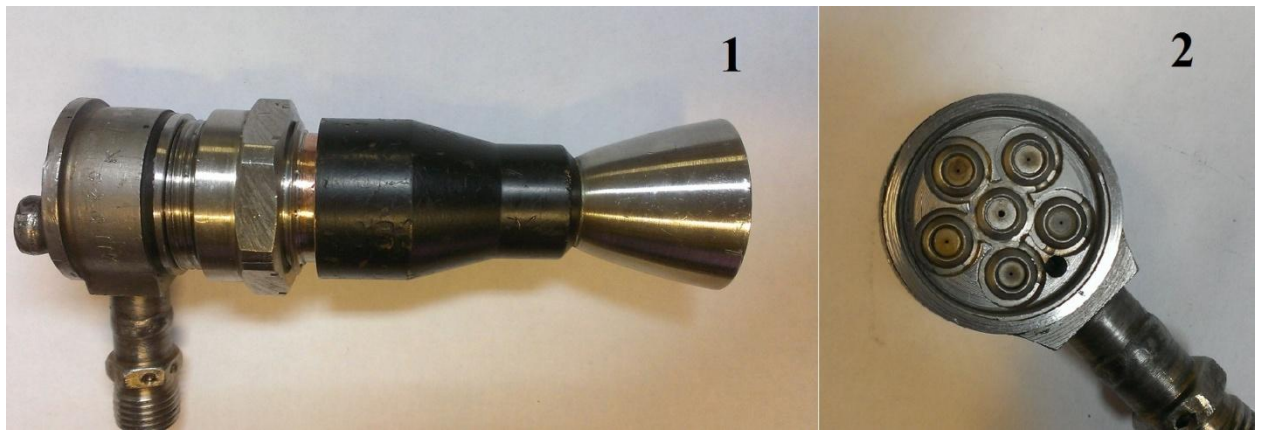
Внешний вид двигателя в сборе - 1; смесительной головки - 2.
